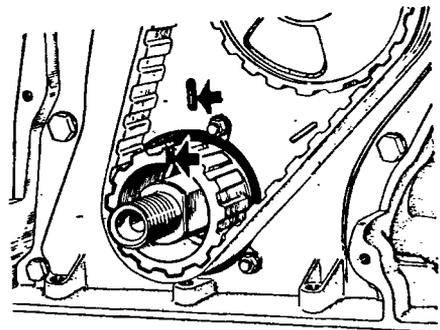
Проверка совпадения установочной метки на шкиве коленчатого вала с меткой на крышке привода распределительного вала
